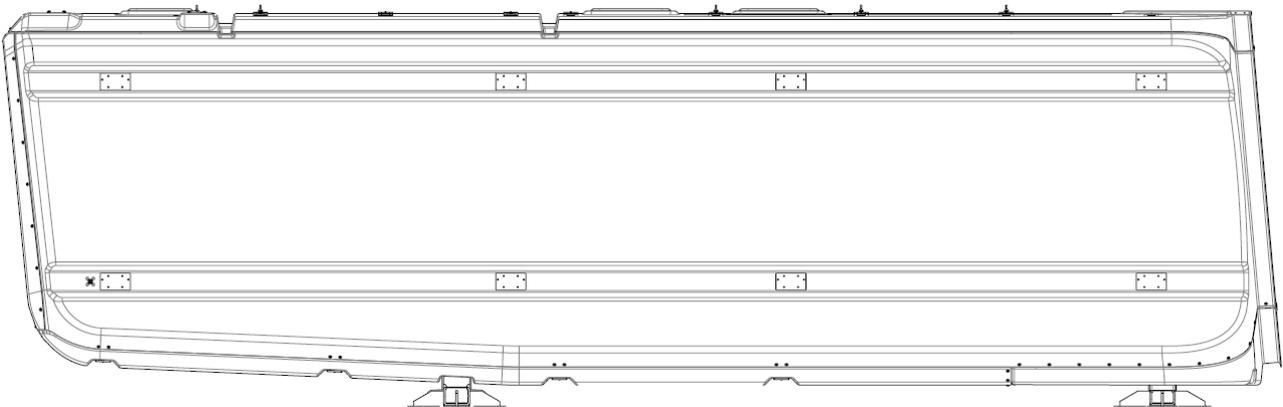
Maschinenhaus (Ansicht von rechts) mit Transportfüßen
